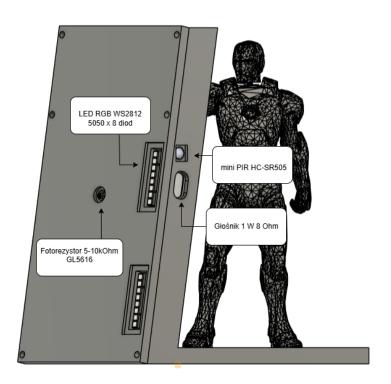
Widok modelu 3D z objaśnieniem elementów projektu (1)
